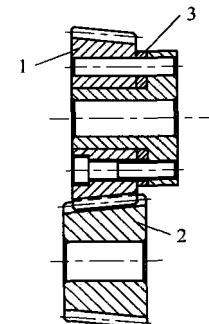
圆柱齿轮轴向垫片间隙消除机构
